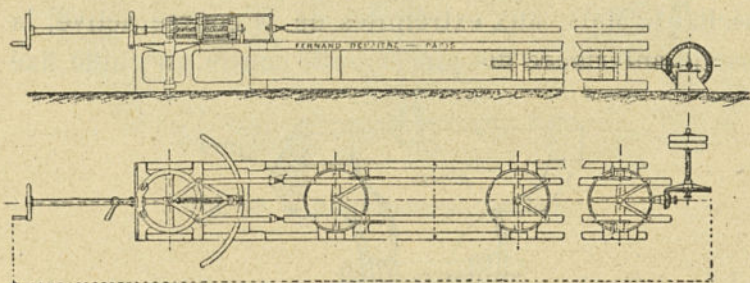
Elévation et plan d'une rame à dérailage (Dehaître).
